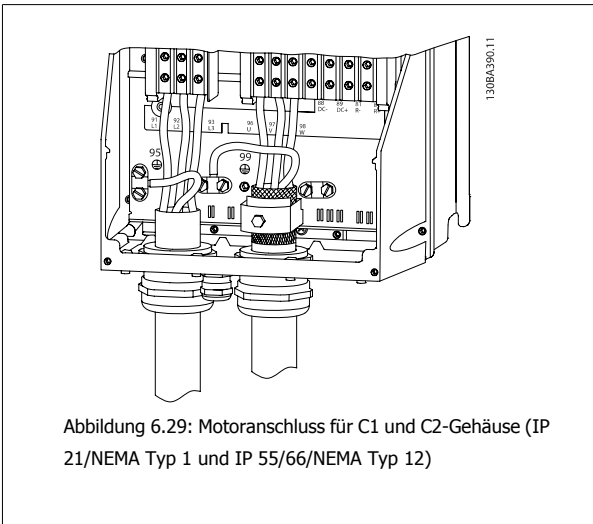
Motoranschluss für C1 und C2-Gehäuse (IP 21/NEMA Typ 1 und IP 55/66/NEMA Typ 12)
